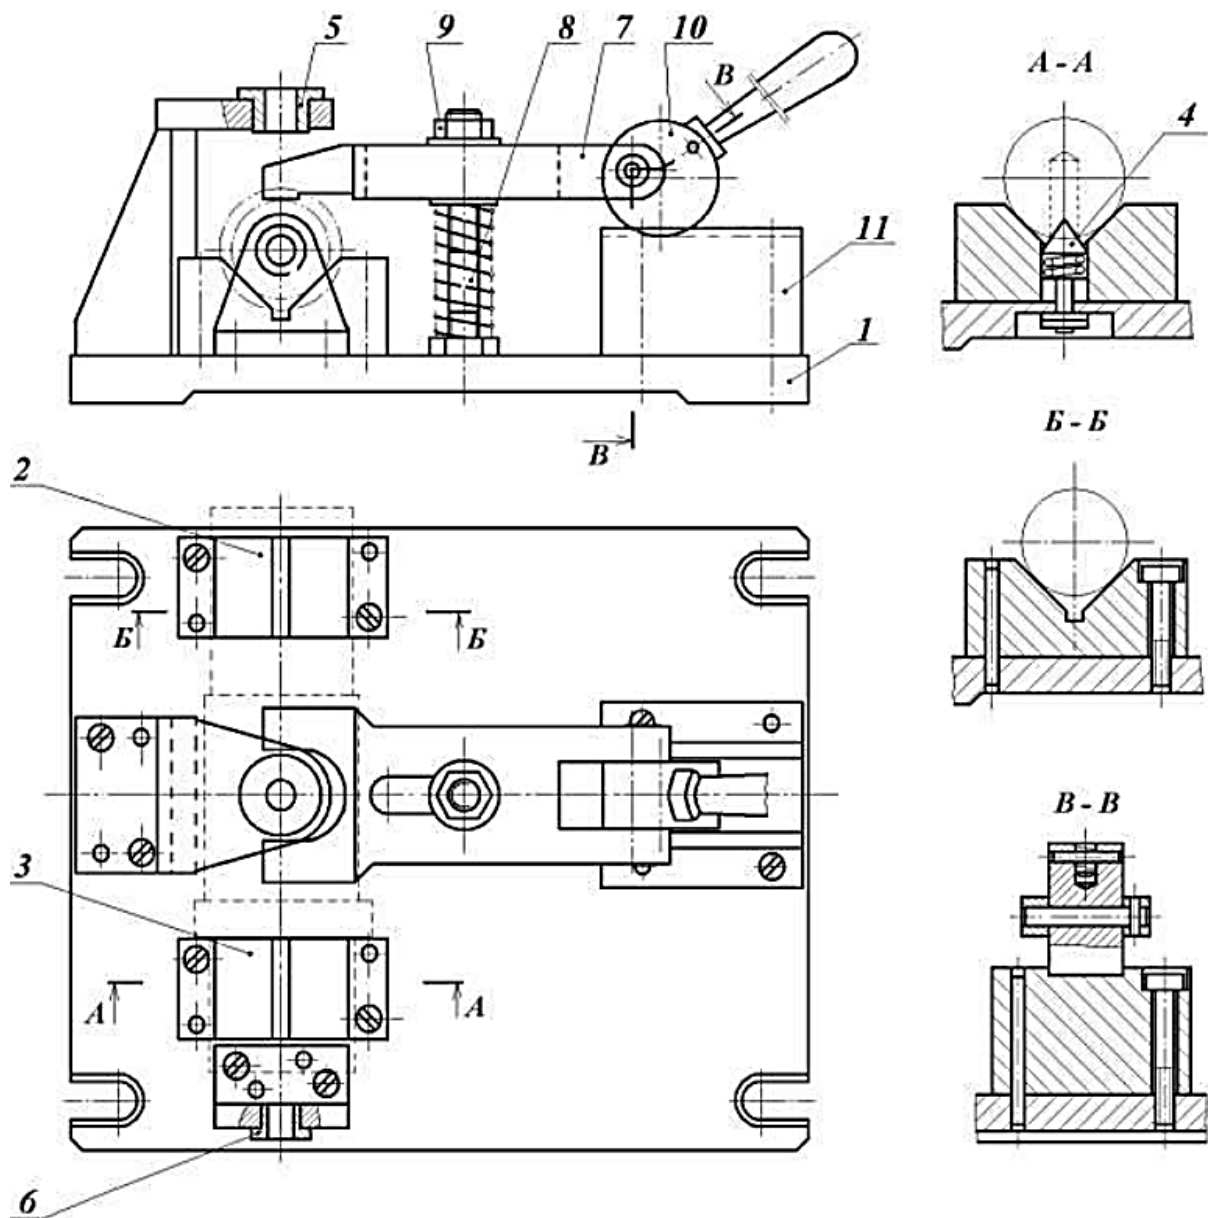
Эскиз сборочного чертежа спроектированного приспособления:
